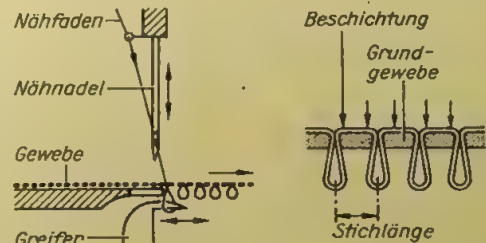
Werkzeuge einer Tuftingmaschine (links), Erzeugnisstruktur (rechts)
